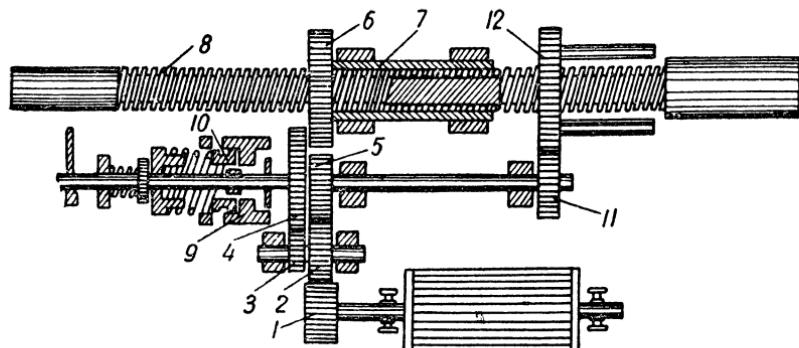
Кинематическая схема электросверла ЭБК-2А
